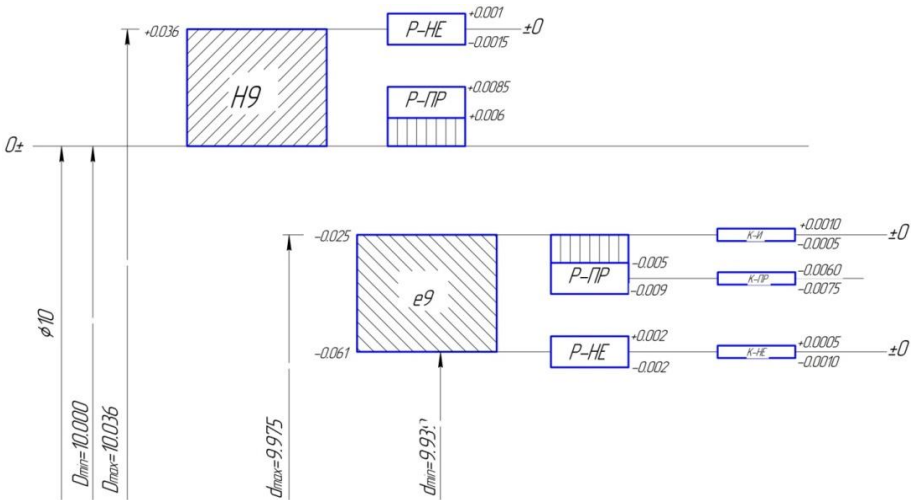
Схема розташування полів допусків калибрів і контракалібрів
